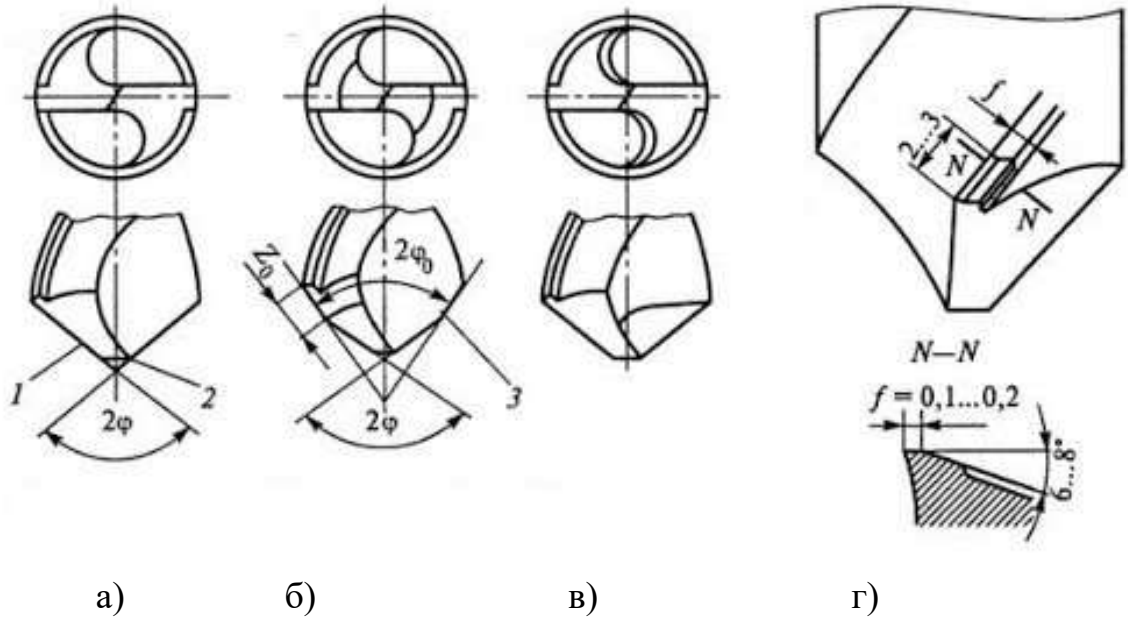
Форми заточування спіральних свердлів: а – звичайне; б - подвійна; в – з підточкою поперечної перемички та стрічки; г - підточування стрічки; 1 - головна ріжуча кромка; 2 – поперечна ріжуча кромка; 3 - допоміжна ріжуча кромка.
